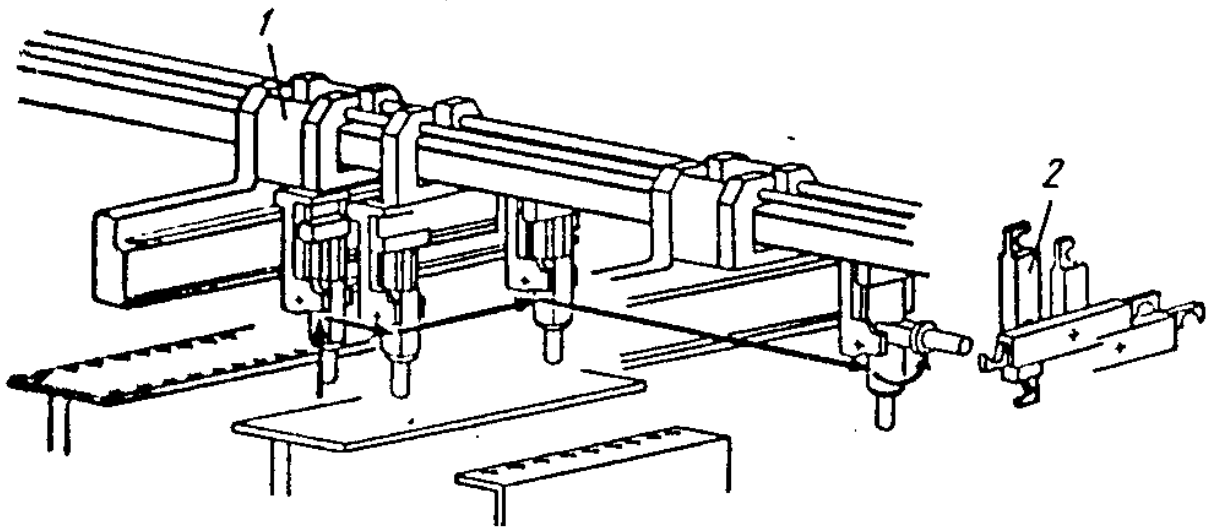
Транспортное приспособление и автооператор смены инструмента
